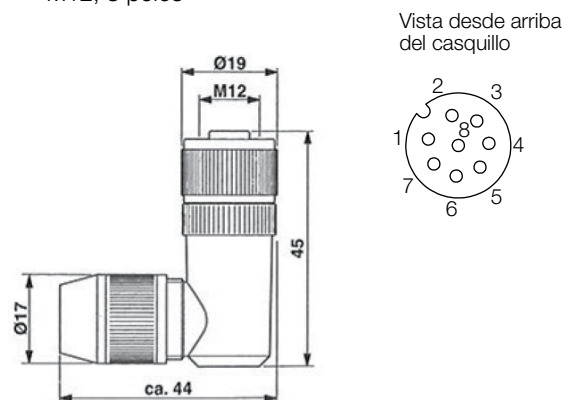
Conector BCC M488-0000-1A-000-43x834-000
